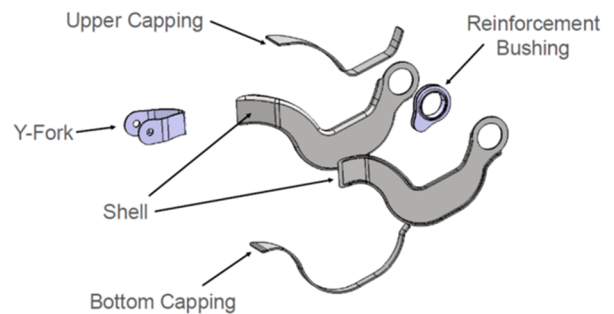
Explosionado de elementos principales del nuevo concepto de camber link que exige alto nivel de integración
